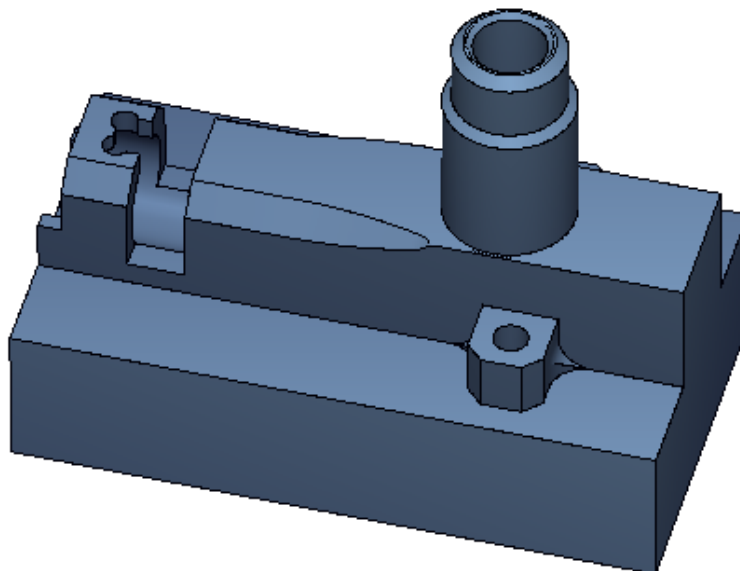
Polotovar po hrubování a frézování čela obrobku.
